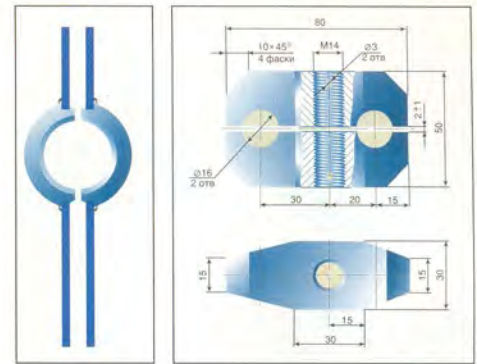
Пластины с полукольцом в сборе (сварка).
